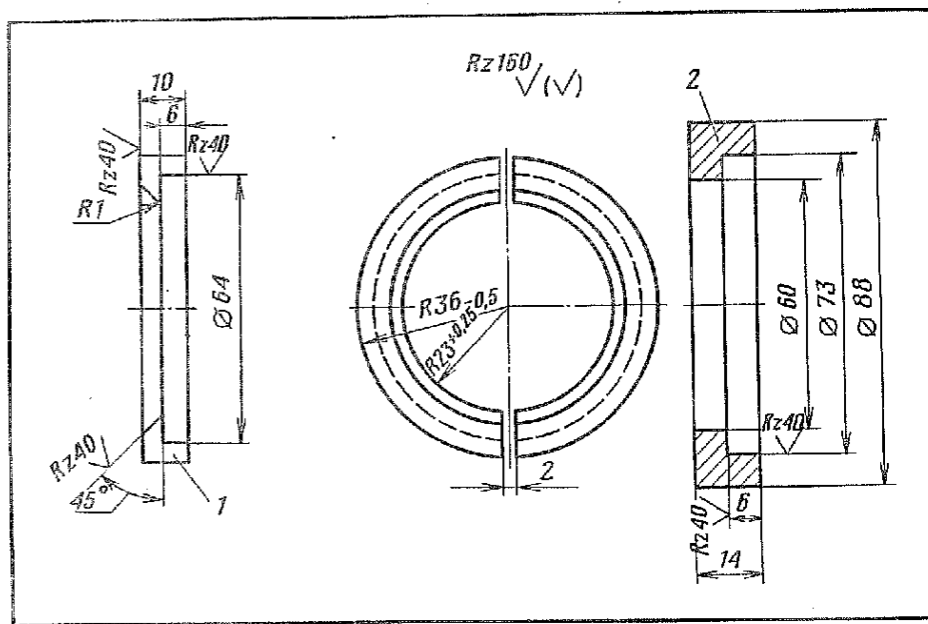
Приспособление для снятия внутреннего кольца подшипника ведущей шестерни главной передачи:
